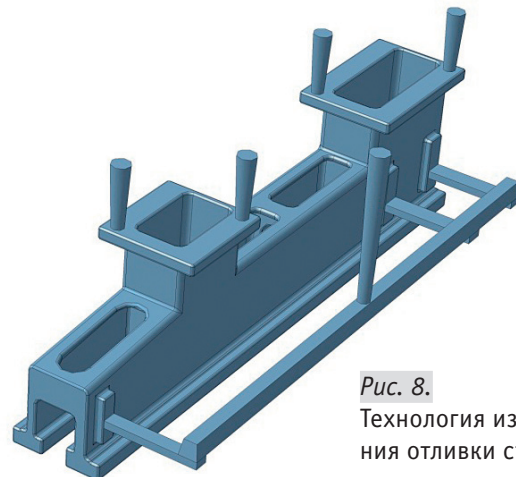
Технология изготовления отливки станины токарного станка ТВ-3
